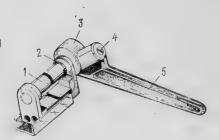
1 — прижим; 2 — насадка; 3 — шпиндель; 4 — винт стопорный; 5 — ручка
